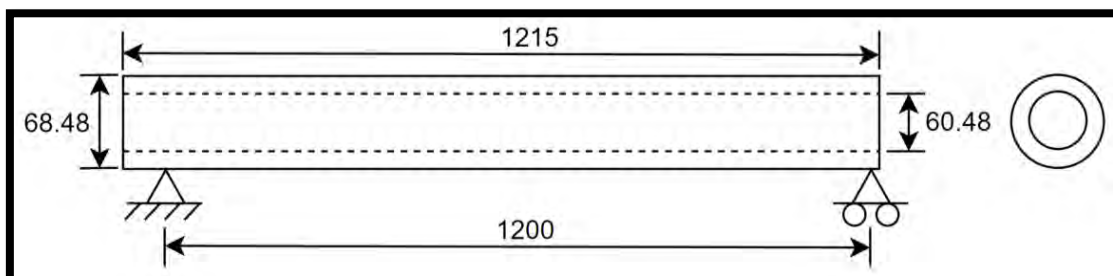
Apoyos y dimensiones de la cámara de fundición.
